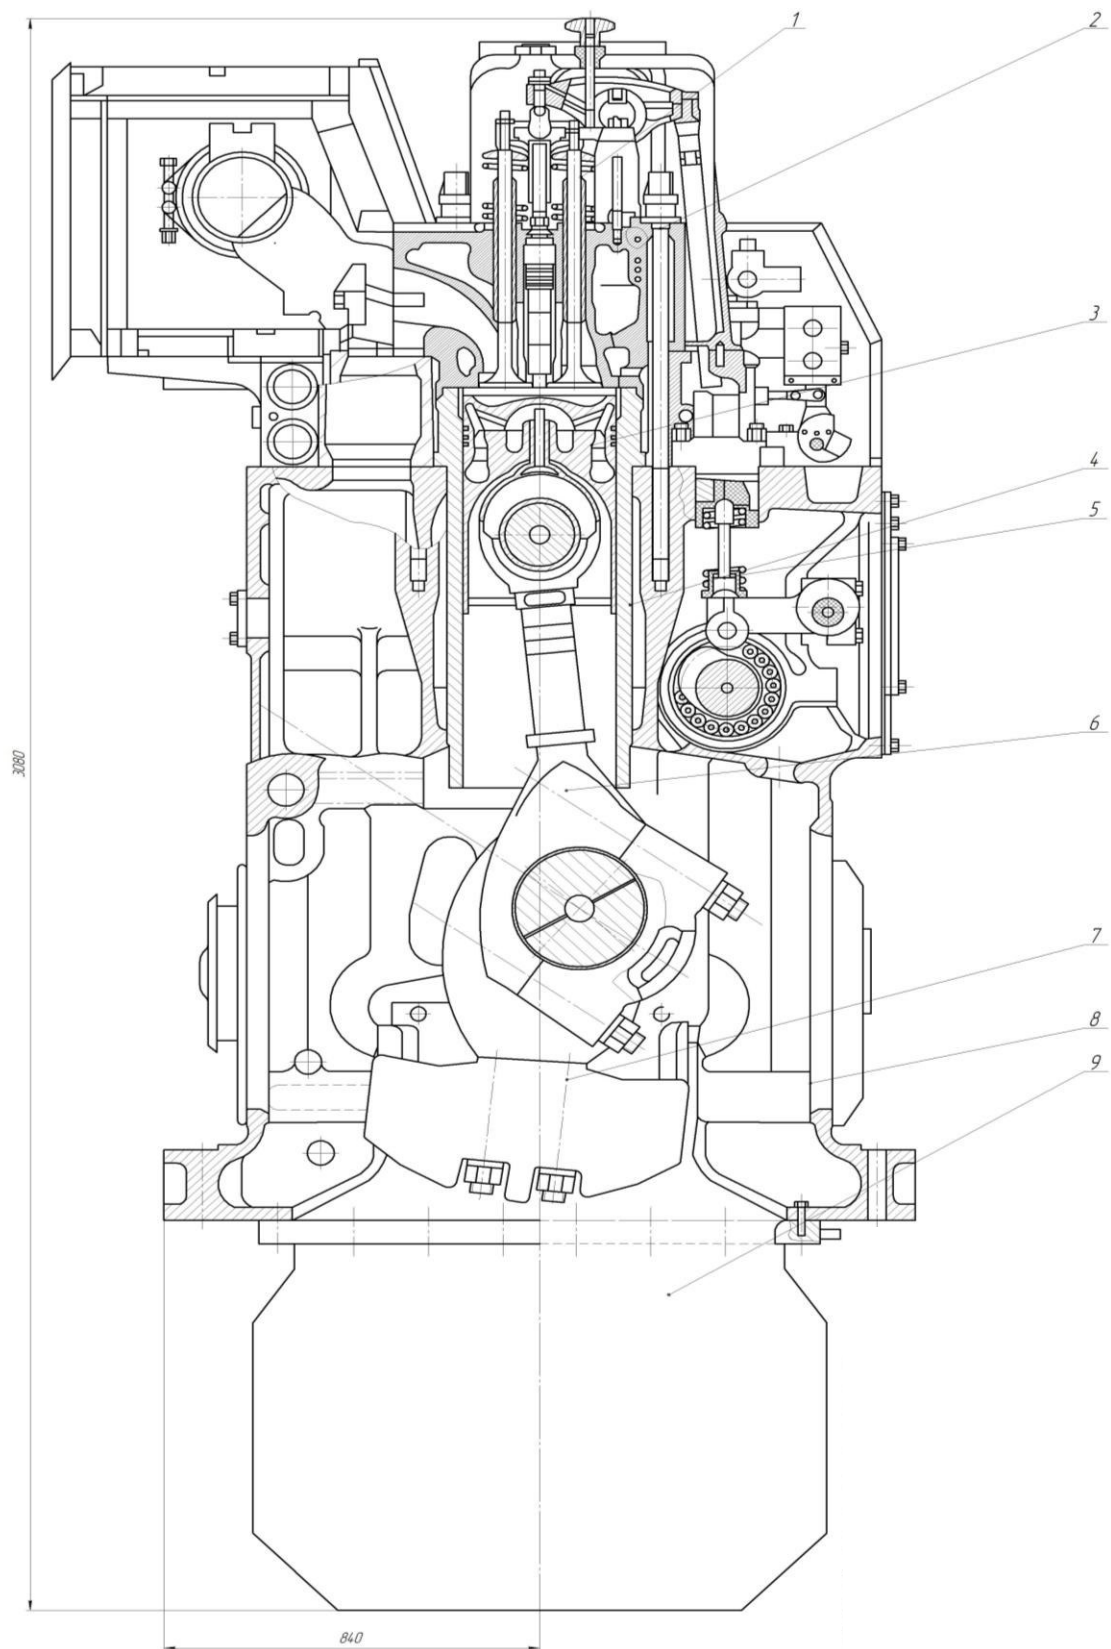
Фронтальний розріз головного ДВЗ: 1 — газорозподільний клапан; 2 — стяжна шпилька; 3 — поршнева група; 4 — робоча втулка; 5 — штовхач паливної помпи; 6 — шатун; 7 — колінчастий вал; 8 — блок-картер; 9 — маслосбірний піддон
